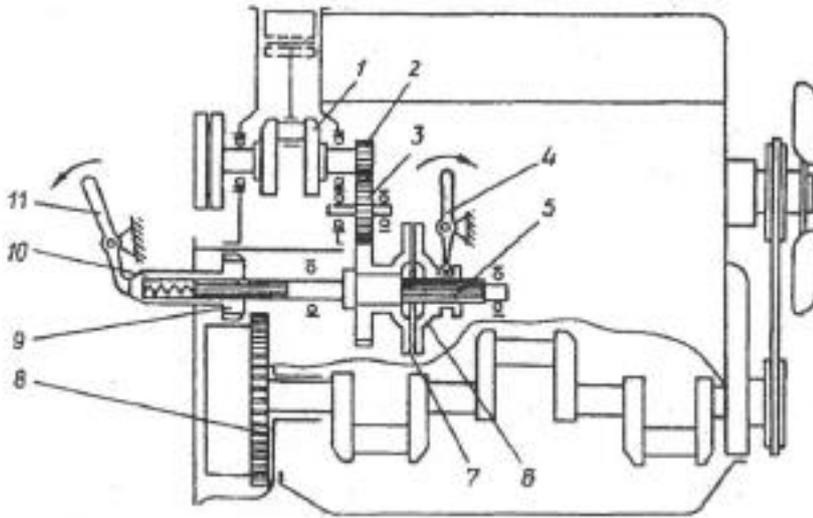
Схема пускового пристрою: 1 - колінчастий вал двигуна; 2, 3 - шестірні; 4 - важіль зчеплення; 5 - вал передавального механізму; 6,7 - відповідно ведений і ведучий диски; 8 - зубчастий вінець маховика дизеля; 9 - пускова шестірня; 10-автомати вимикання; 11 - важіль вмикання пускової шестірні
